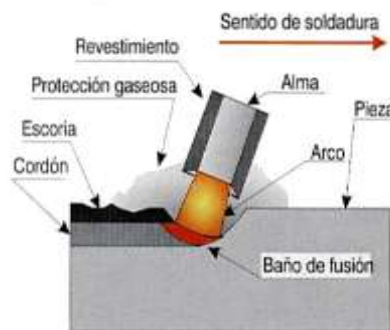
Tablero didáctico en el proceso de soldadura
